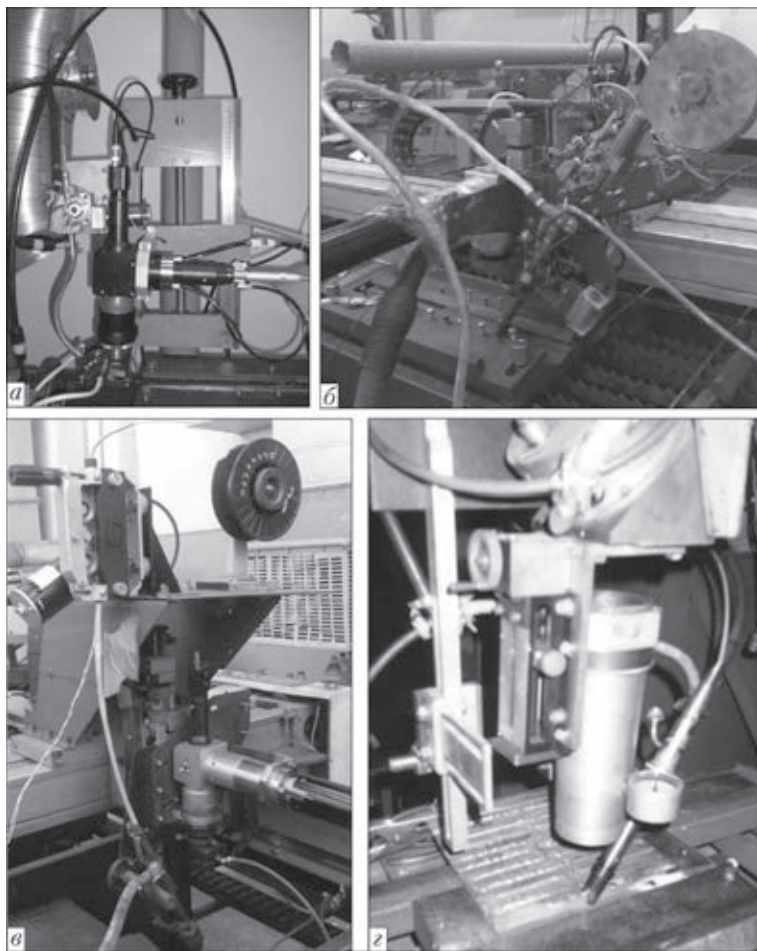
Внешний вид головок для гибридной лазерно-дуговой сварки, осуществляемой при помощи одно- или трехкоординатного манипулятора, разработанных в ИЭС им. Е.О. Патона: а–в — для лазеров с длиной волны до 1,06 мкм; г — 10,6
